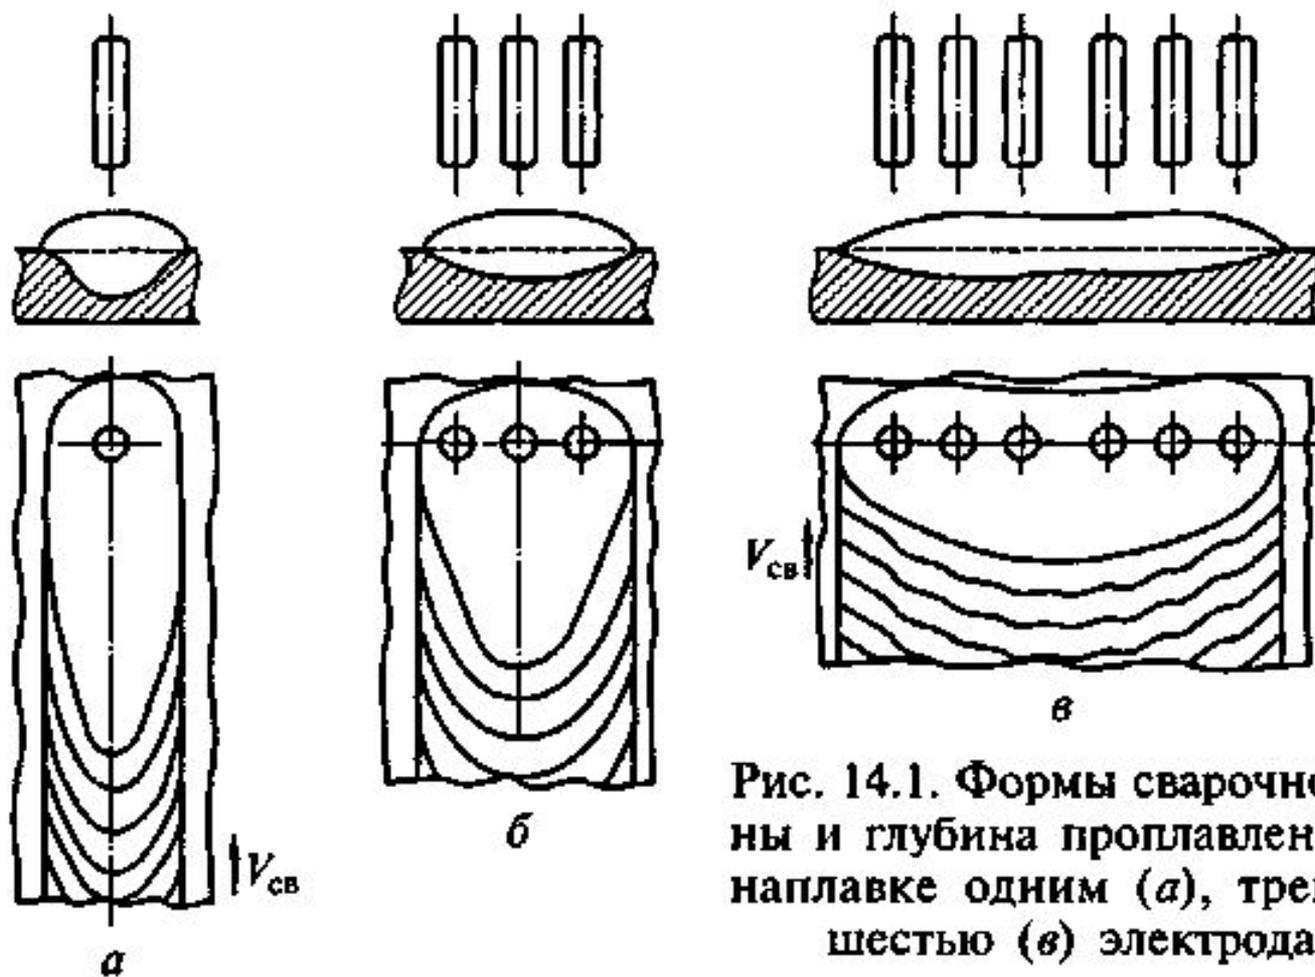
Формы сварочной ванны и глубина проплавления при наплавке одним (*a*), тремя (*б*), шестью (*в*) электродами
